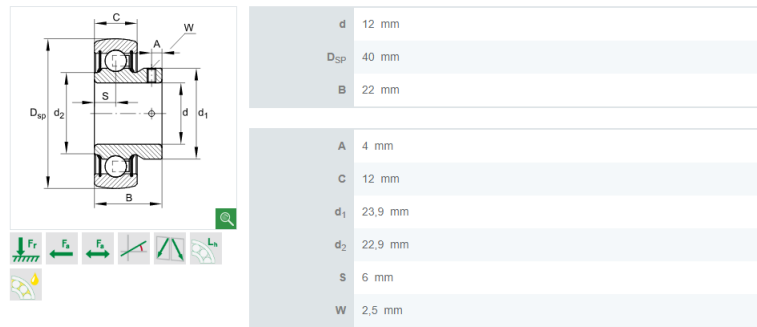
26. Rodamientos insertables AY12-XL-NPP-B
